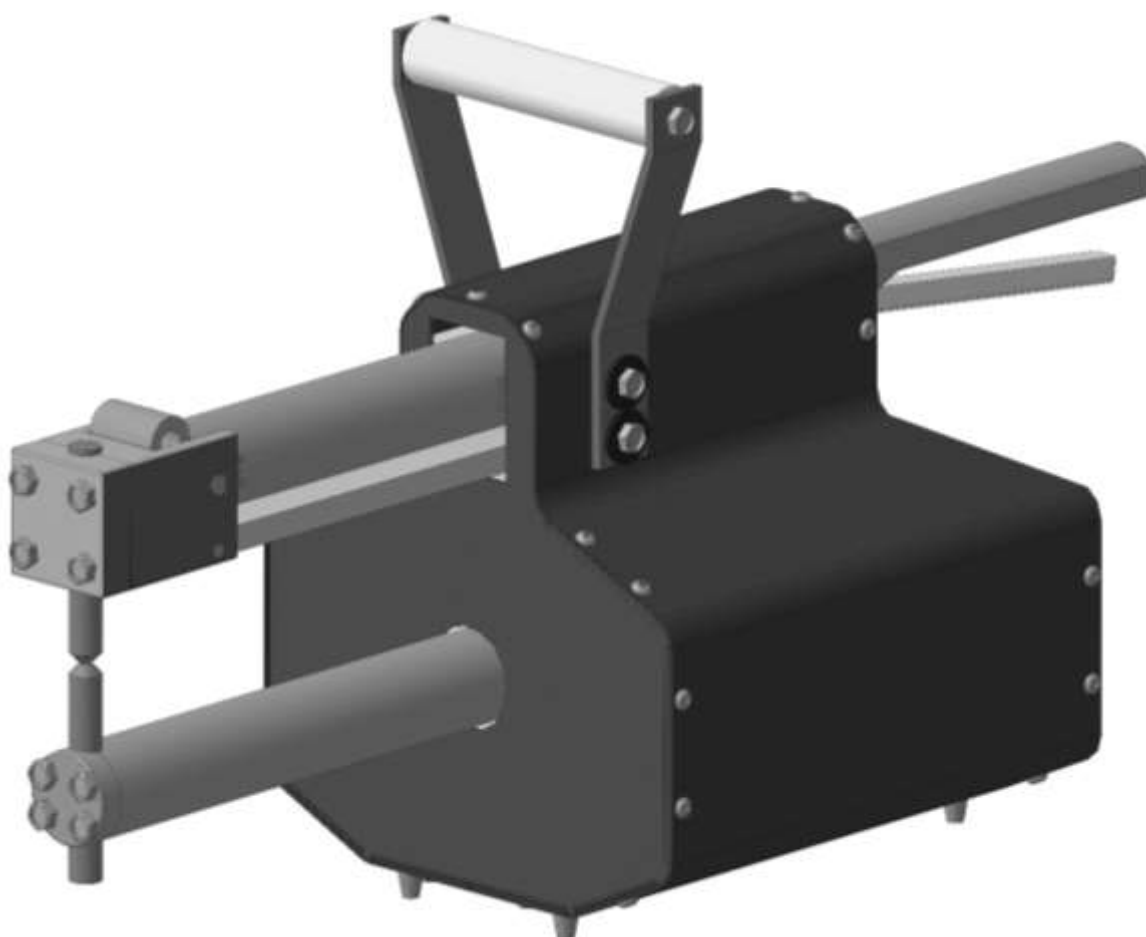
Клещи для контактной точечной сварки в сборе.
